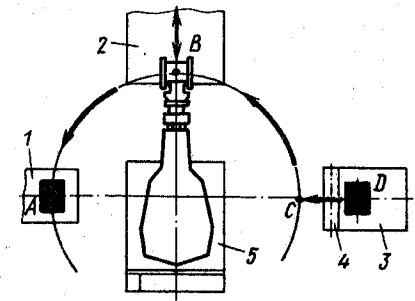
Схема оборудования промышленным роботом конвейера и двух станков
